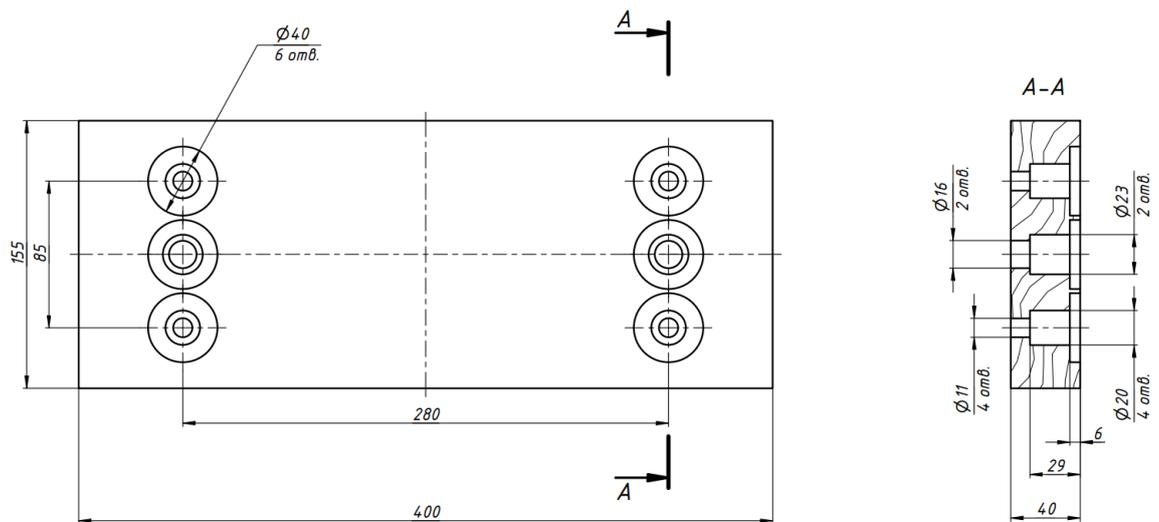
Рабочий чертеж подвижных губок тисков Моксона
